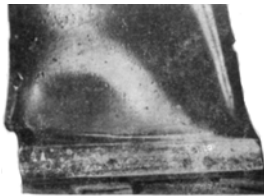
Утворення тріщини в кореневій частині робочої лопатки компресора
